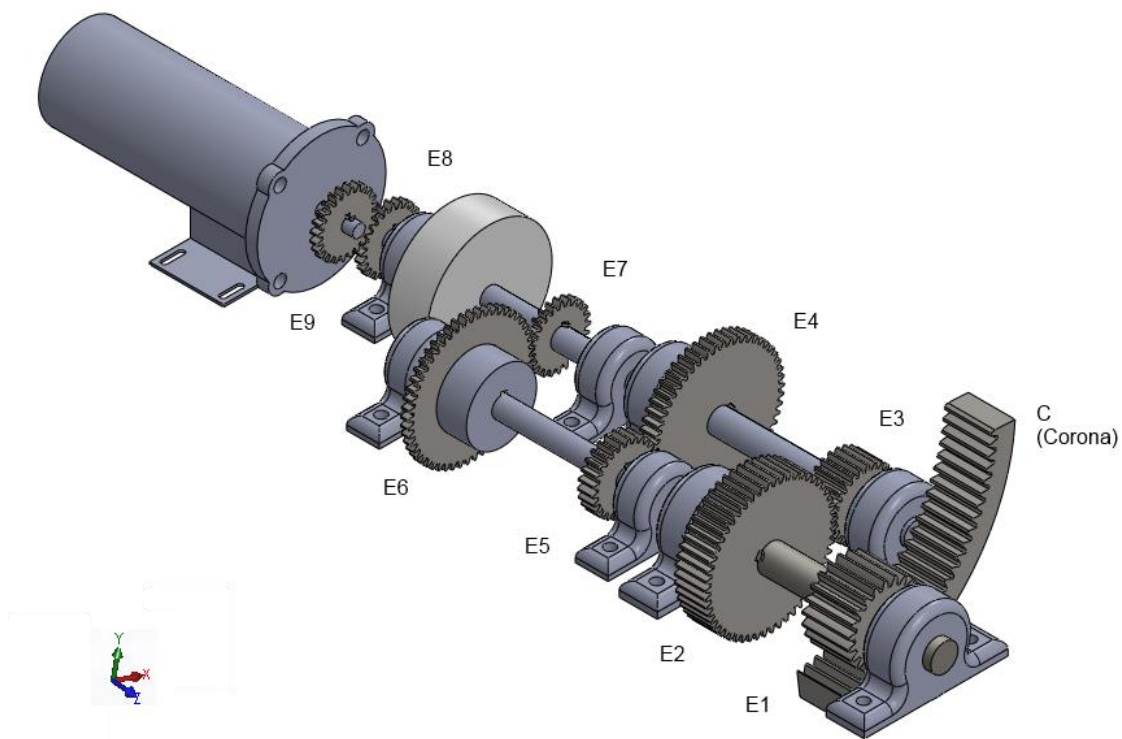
Vista isométrica del sistema de engranajes. Fuente: Elaboración propia.
